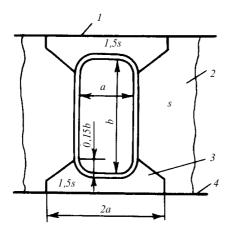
1 — палуба; 2 — стенка рубки; 3 — утолщенный лист; 4 — расчетная палуба
